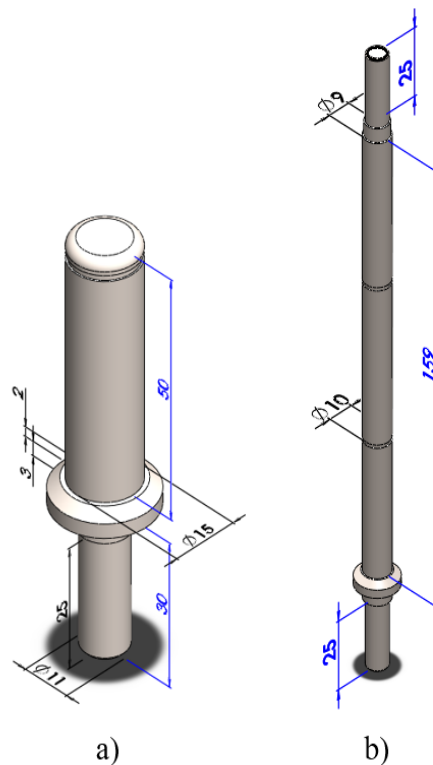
a) Dimensões do eixo das rodas laterais; b) Dimensões do eixo do rolo (mm).
